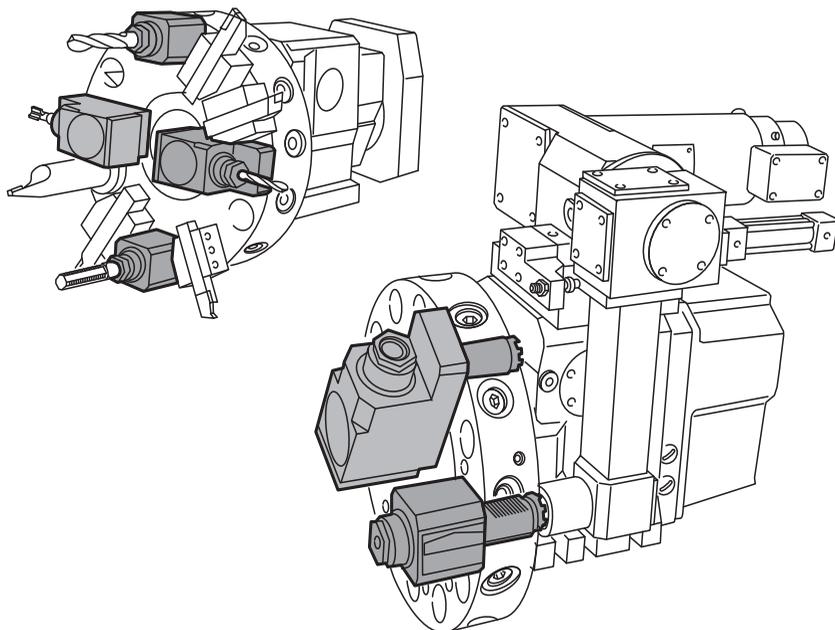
Револьверные головки с неподвижными и вращающимися инструментами
